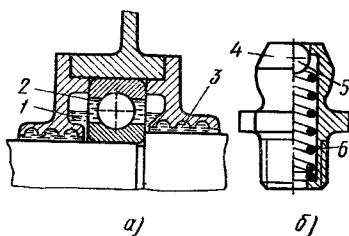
Размещение смазки в подшипниковой опоре (а) и шариковая пресс-масленка (б)
